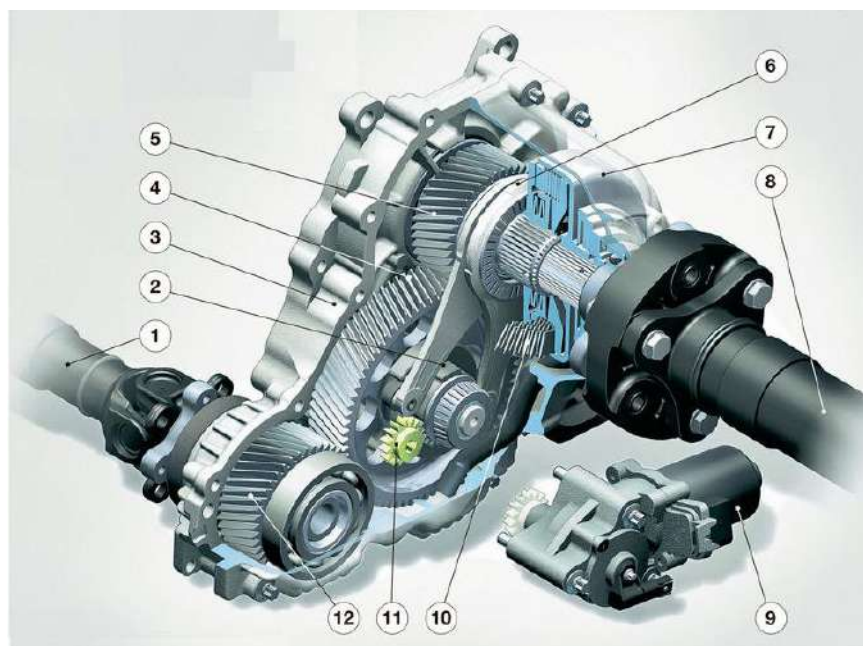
Конструкция раздаточной коробки xDrive с приводными шестернями
